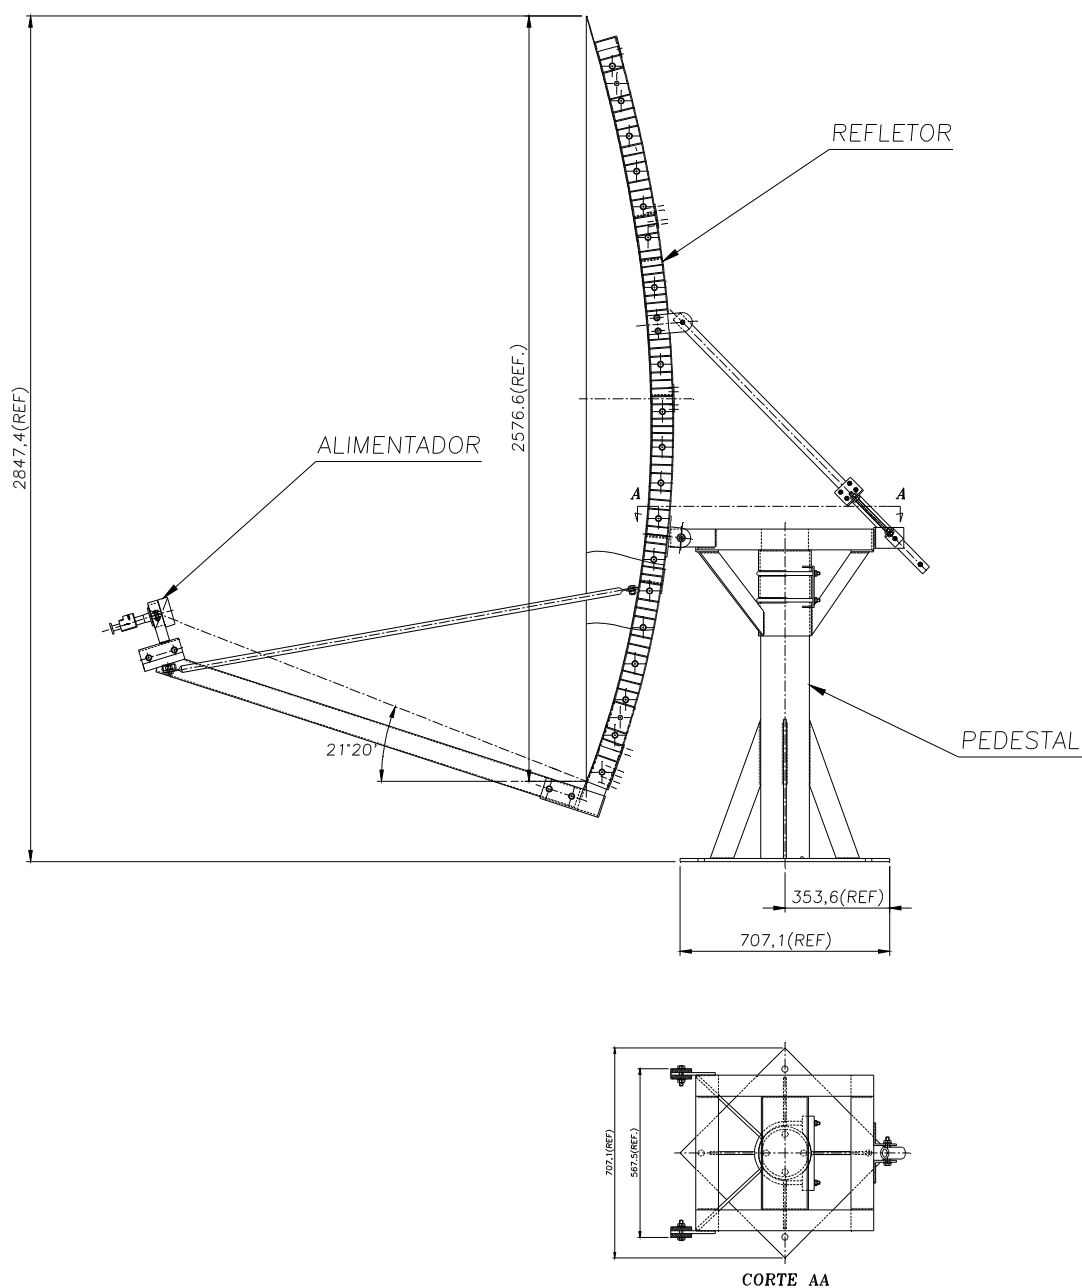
CONJUNTO / DIMENSÕES GERAIS
